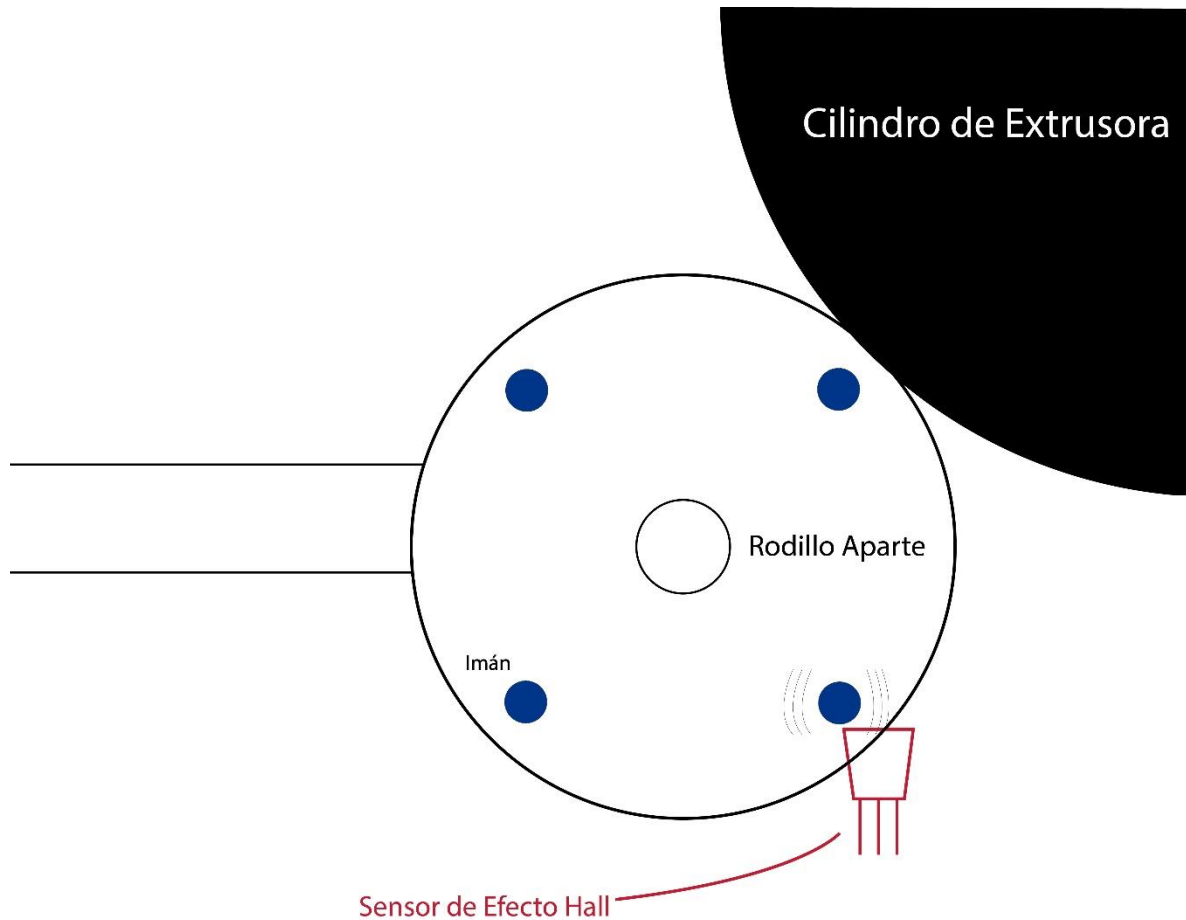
Representación del sensor sobre un rodillo aparte. Fuente: Elaboración propia.
